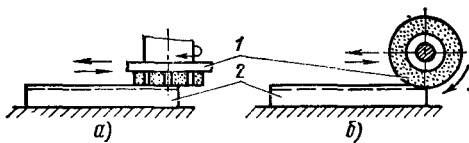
Схемы плоского шлифования: а - торцом шлифовального круга; б - периферией шлифовального круга; 1 - шлифовальный круг; 2 - деталь
